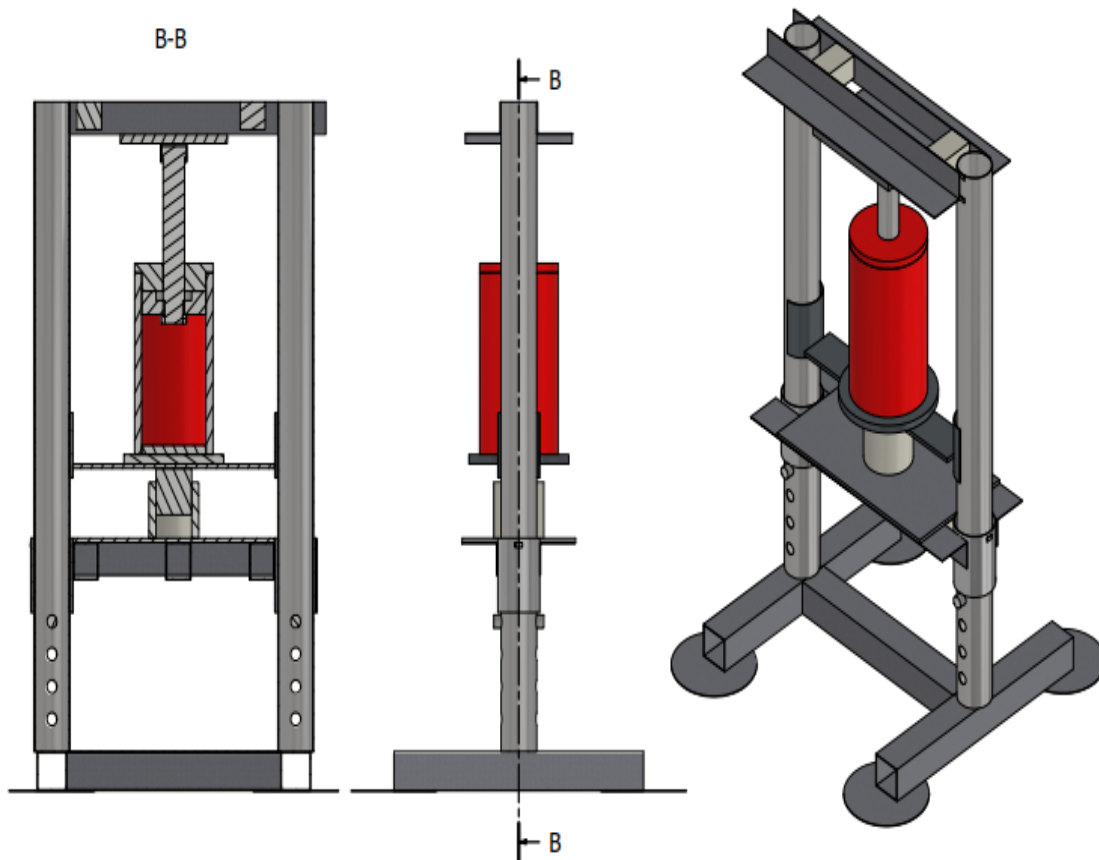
Boceto del diseño de una máquina compactadora de viruta (Imagen propia).
